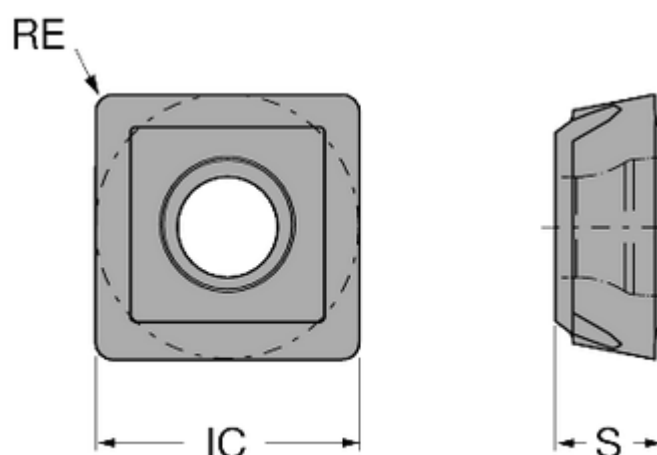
Пластинка ріжуча 880-08 05 W12H-P-GR 4334
